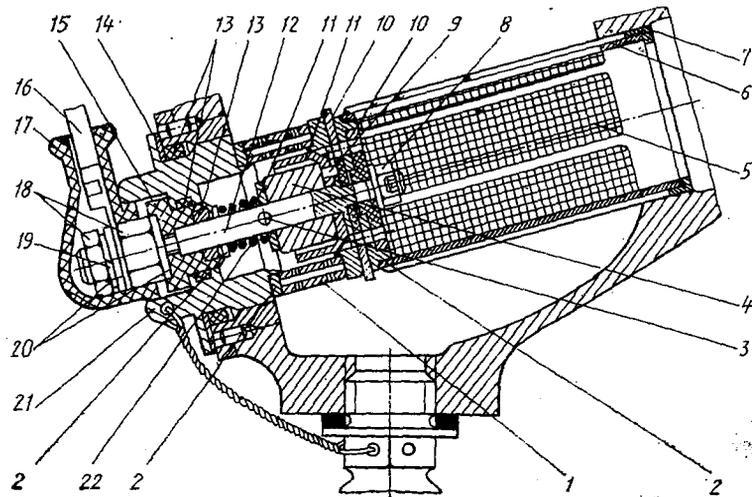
а. Фильтр-сигнализатор стружки двигателя АШ-62ИР 17 сер. (ТК № 38а, вып. 2—4): 1—блок пластинок; 2—прокладка; 3—штифт; 4—постоянный магнит; 5—сетка; 6—каркас фильтра; 7—втулка; 8—гайка; 9—штифт; 10—текстолитовая прокладка; 11—полюсный наконечник; 12—стойка-контакт; 13—уплотнительная резиновая прокладка; 14—алюминиевая шайба; 15—изоляционная втулка; 16—наконечник электропровода; 17—резиновый колпачок; 18—гайка; 19—пружинная шайба; 20—шайба; 21—гайка фильтра; 22—прижимная пружина;
